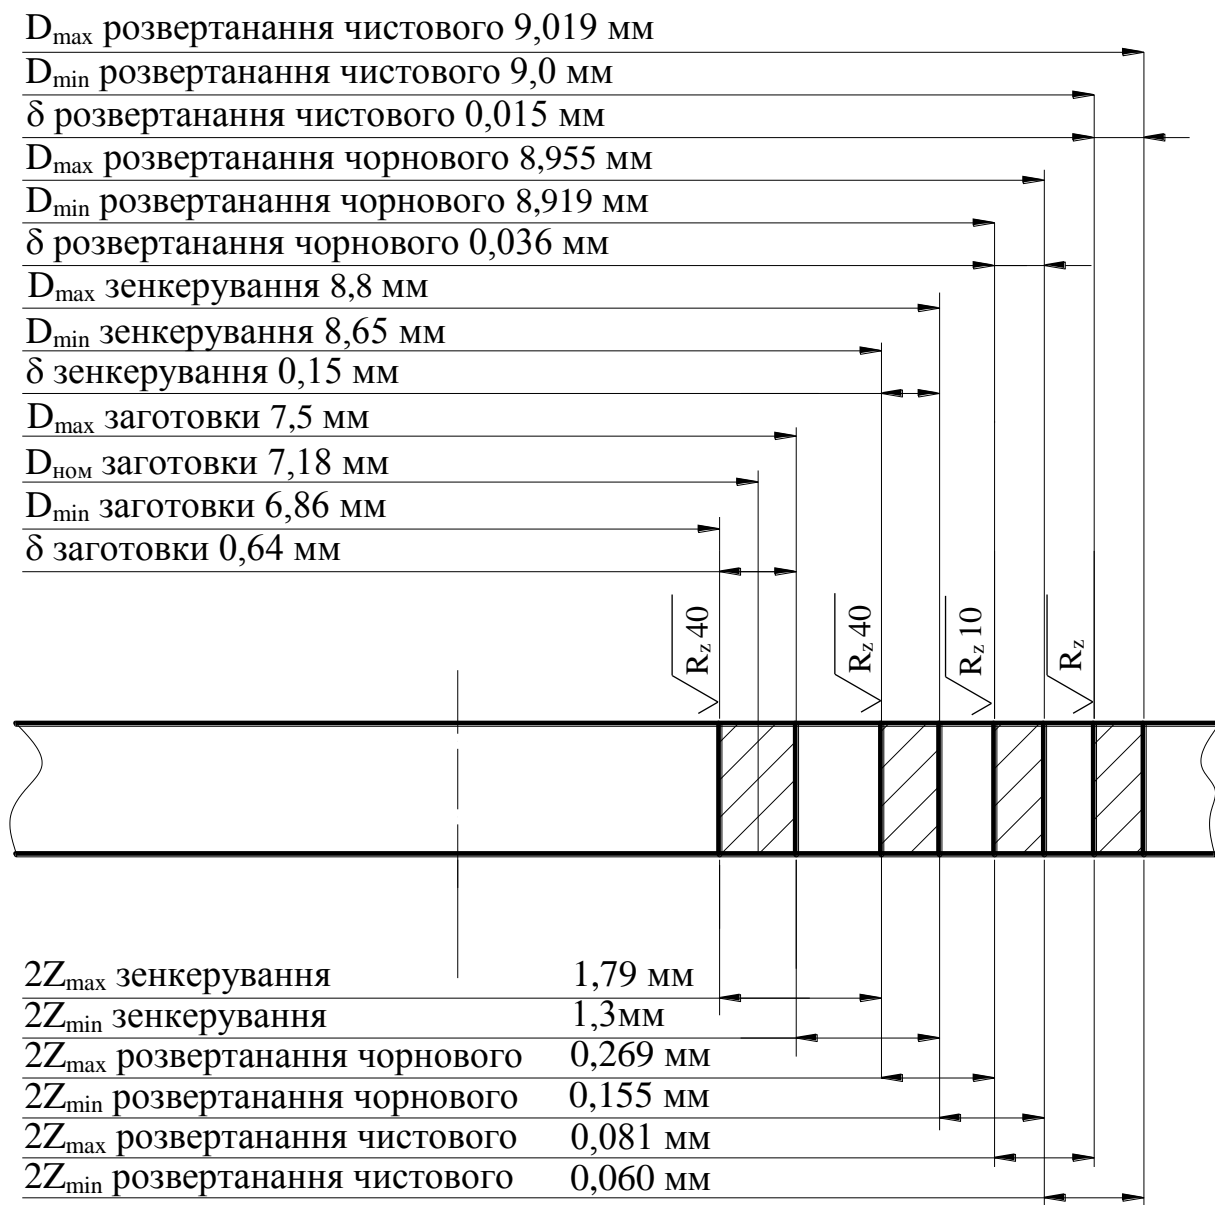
Схема графічного розташування припусків  $\varnothing 9H7$
